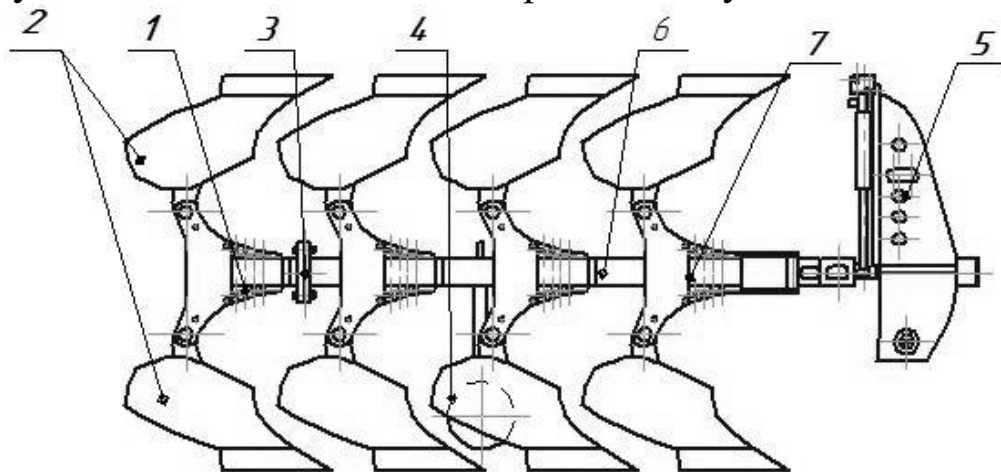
Схема гидрорычажного механизма оборотного плуга
